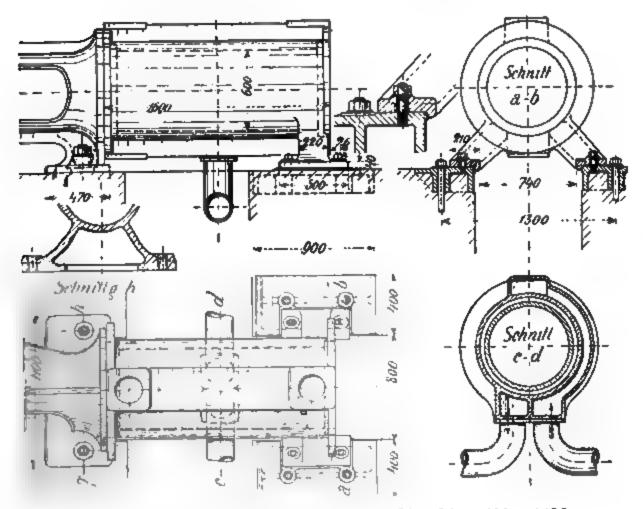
1265. Dampfeylinder für Maschine 600×1050 .
